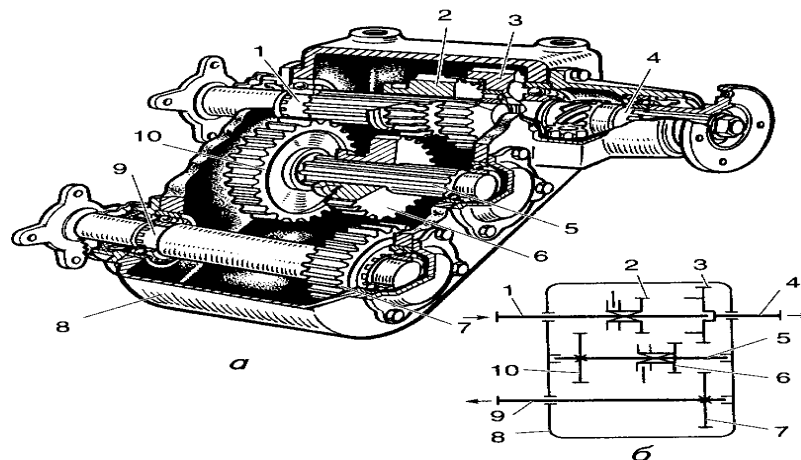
Роздавальна коробка з прямою та знижувальною передачами:
